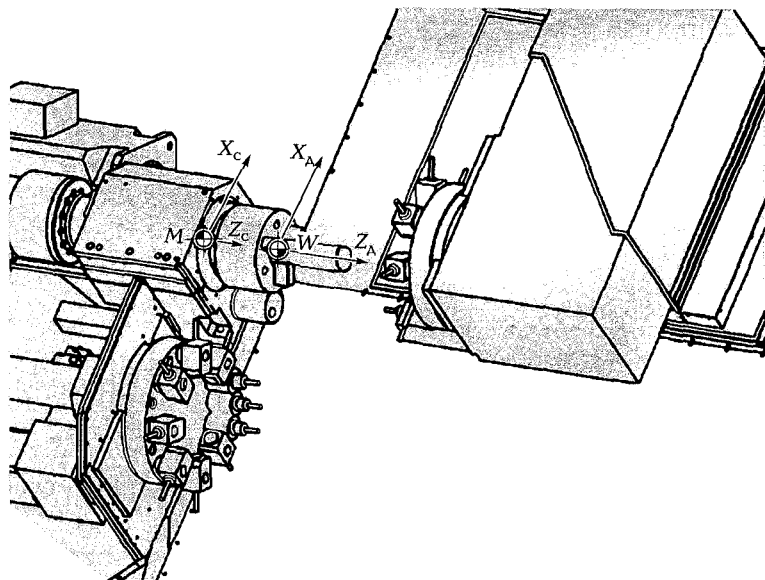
Положение нулевой точки W детали в системе координат токарного станка
